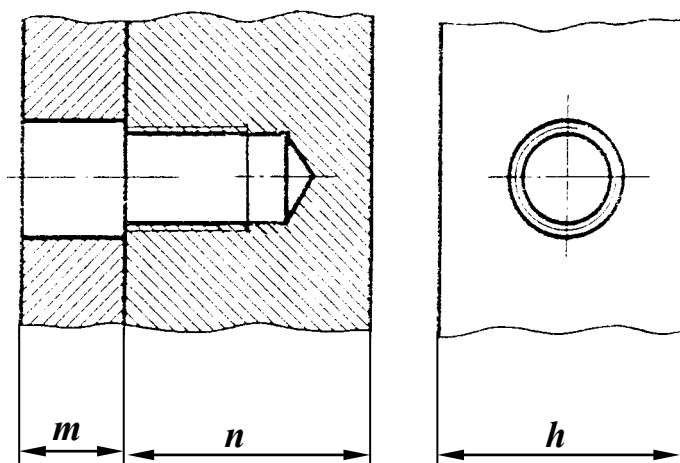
Условное обозначение размеров соединяемых деталей к чертежу «Соединение шпилькой»
